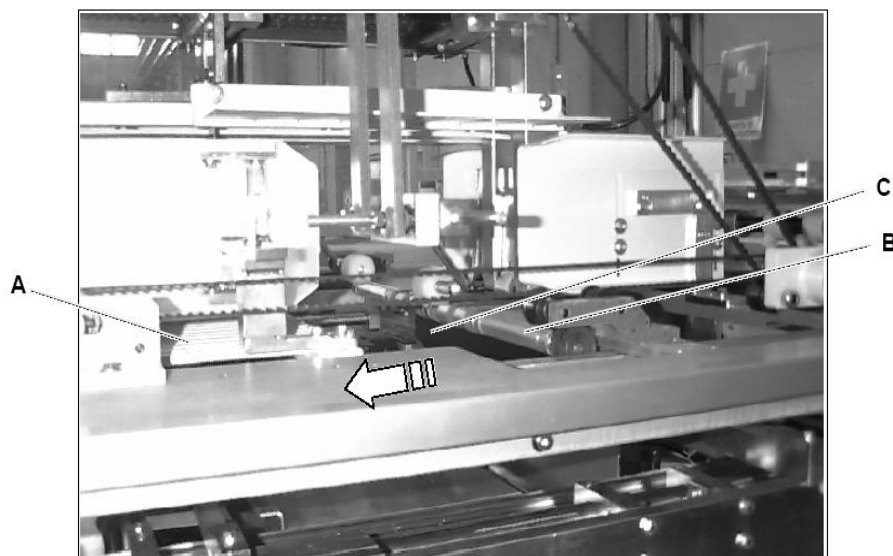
Esquema plegadores y soldadores Inferiores.
